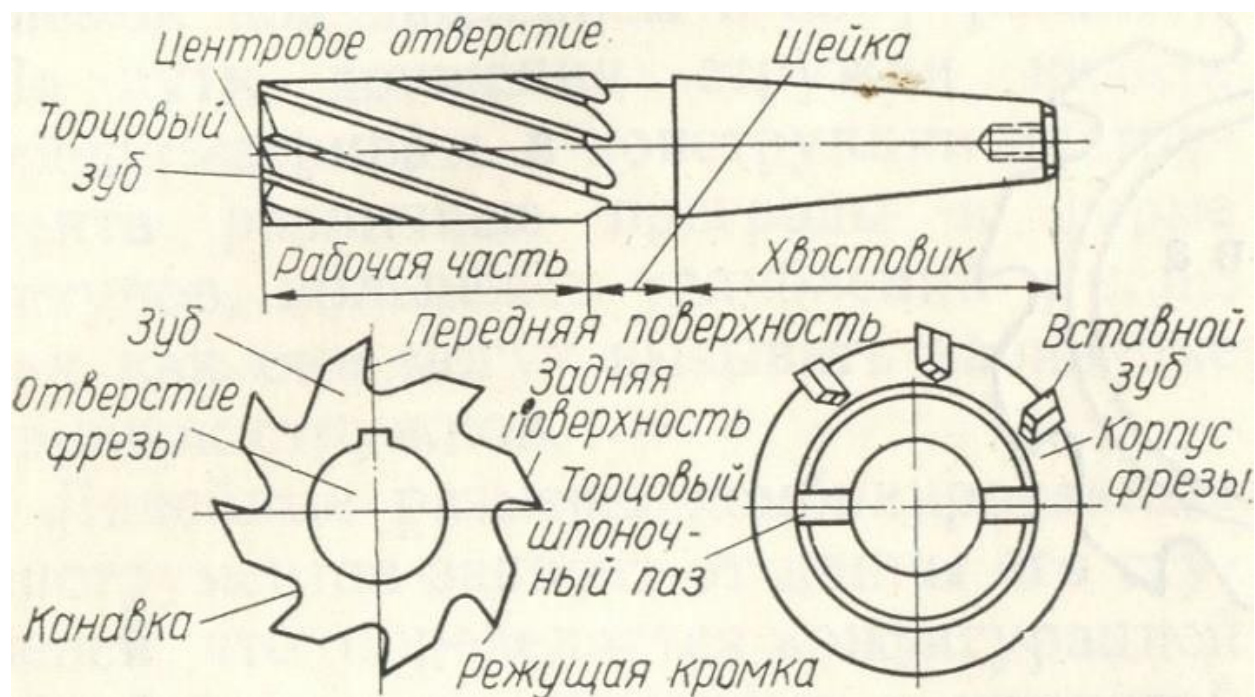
Конструкция концевой фрезы с коническим хвостовиком (вверху) и насадная фреза (внизу)
